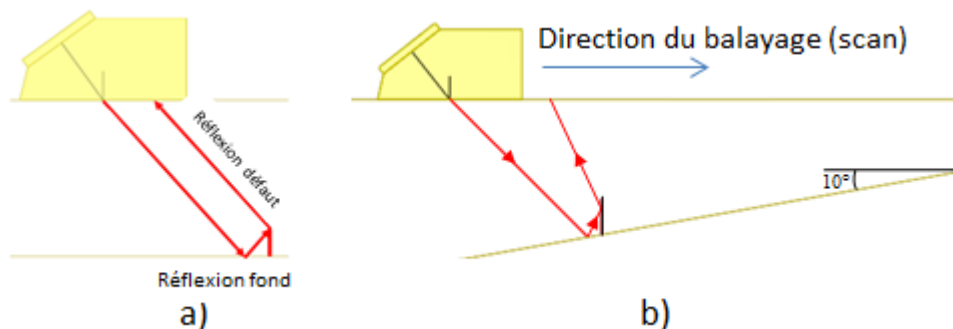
génération d'un écho de coin pour un défaut vertical débouchant sur le fond a) d'une pièce plane et b) d'une pente inclinée de 10° .
